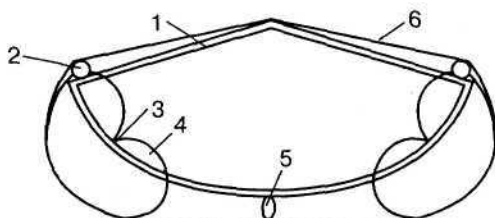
Поперечный разрез КНБ-81: 1 — шпангоут; 2 — привальные брусья; 3 — опорные тросики; 4 — баллоны; 5 — кильсон; 6 — оболочка
